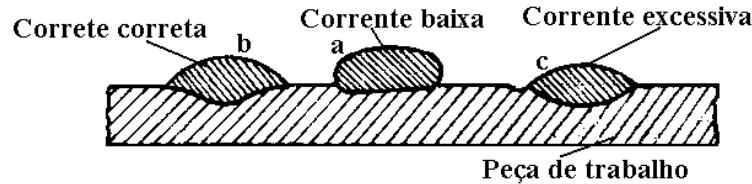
Efeito da corrente de soldagem na penetração do cordão.
